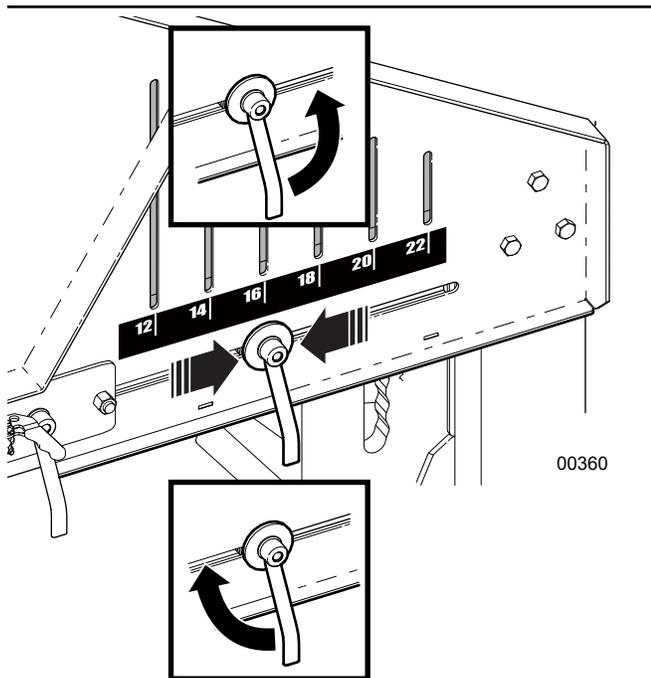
Poignée de verrouillage du guide de butée des grumes
